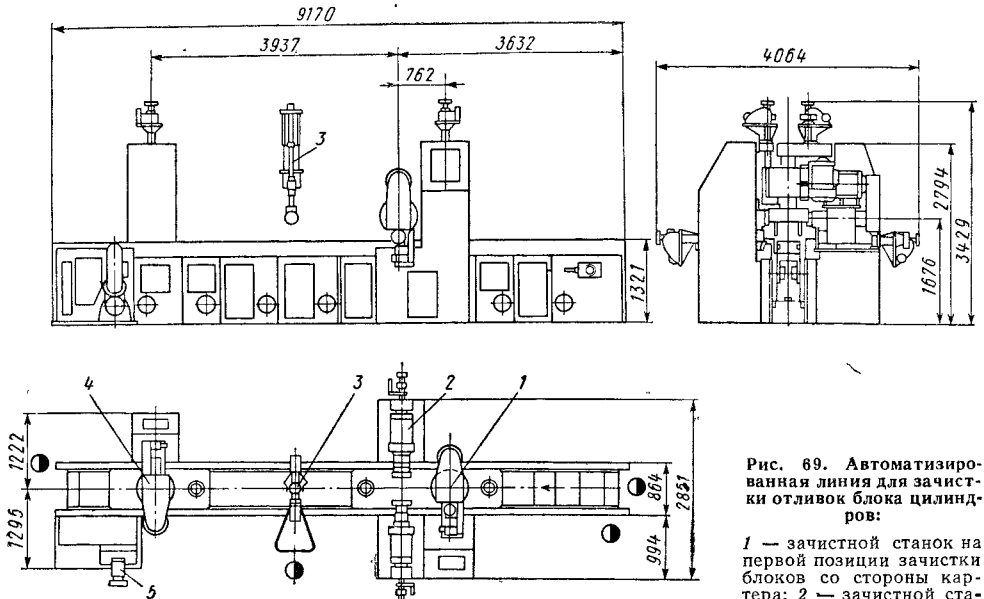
Автоматизированная линия для зачистки отливок блока цилиндрической формы:
